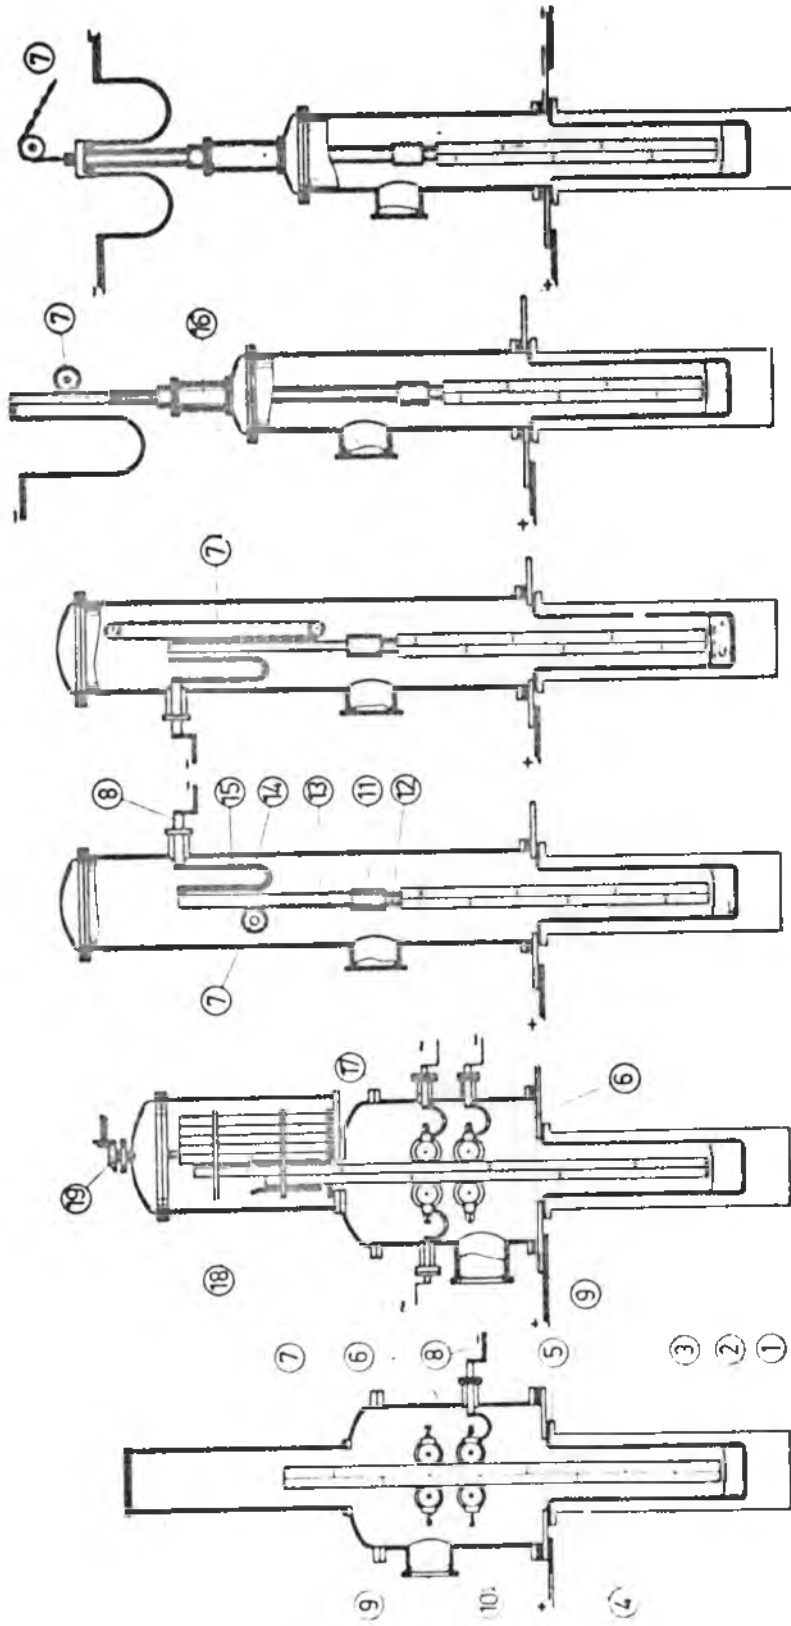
Vista esquemática de una caja de soldadura automática en atmósfera inerte.
